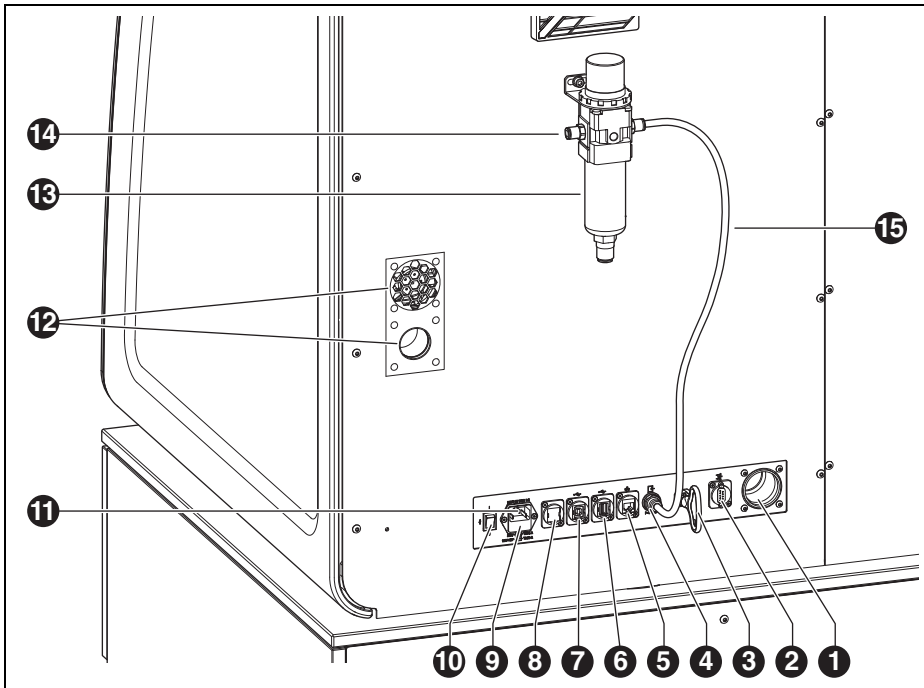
Vue d'ensemble du côté arrière du système de fraisage
